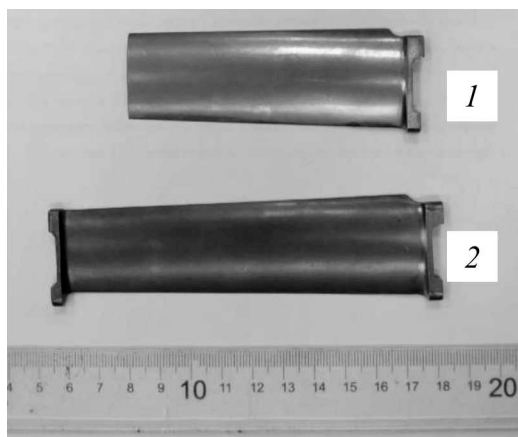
Вид опытной лопатки компрессора низкого давления, полученной из УМЗ-сплава ВТ6 (1), и образца для усталостных испытаний (2)
